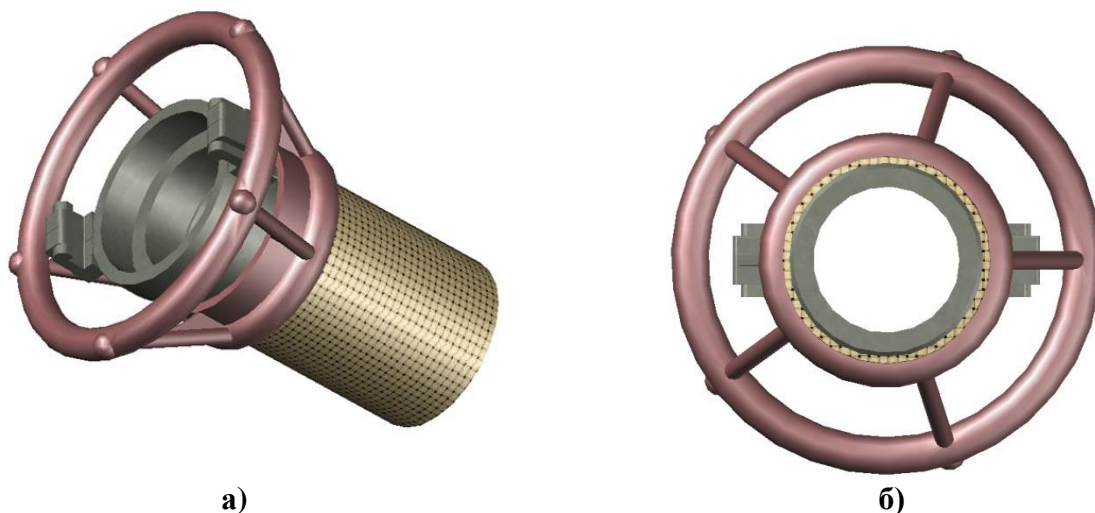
Пожарная соединительная рукавная головка с резиновым буфером:
